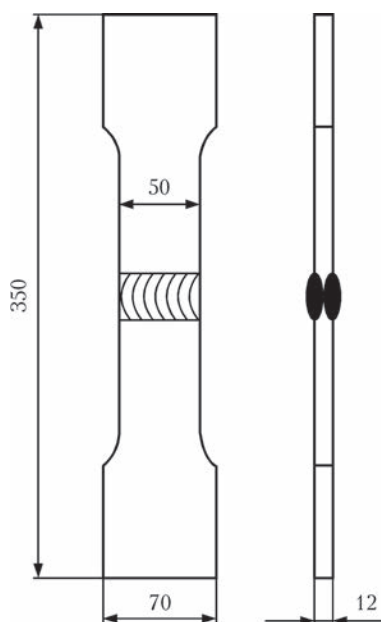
Форма и геометрические размеры образцов стыкового сварного соединения
